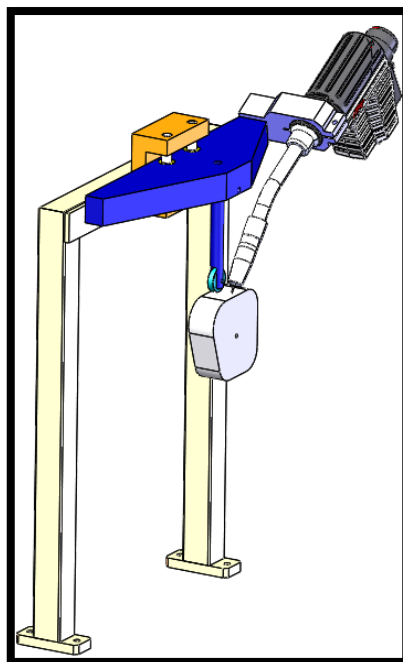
Seguidor de perfil, aplicación de soldadura.
